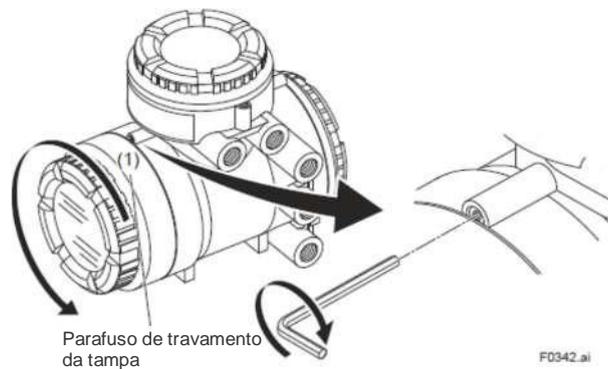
Removendo a tampa da tela (Transmissor Remoto AXG4A)
